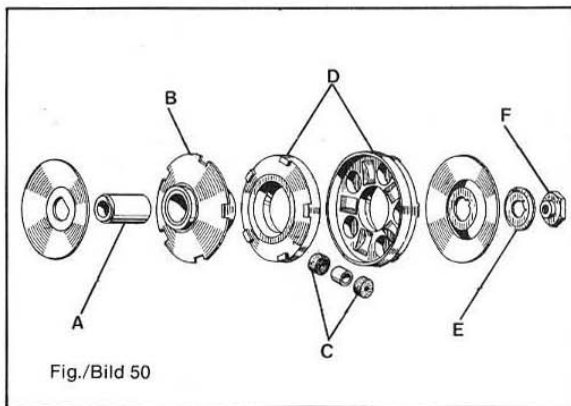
Revision der Getriebeautomatik - Antriebsriemenscheibe: Die Gruppe vom Fahrzeug abbauen (siehe S. 47 des Abschnittes "Ausbau") die Bestandteile, Z. B. die Buchse "A", das Bronzelager der Reglerscheibenhälfte "B", die Rollenüberzüge "C" usw. auf Verschleiß prüfen und falls nötig ersetzen; die Rollenbehälter "D" die Rollen und die Buchse "A" einfetten (s. S. 9).
